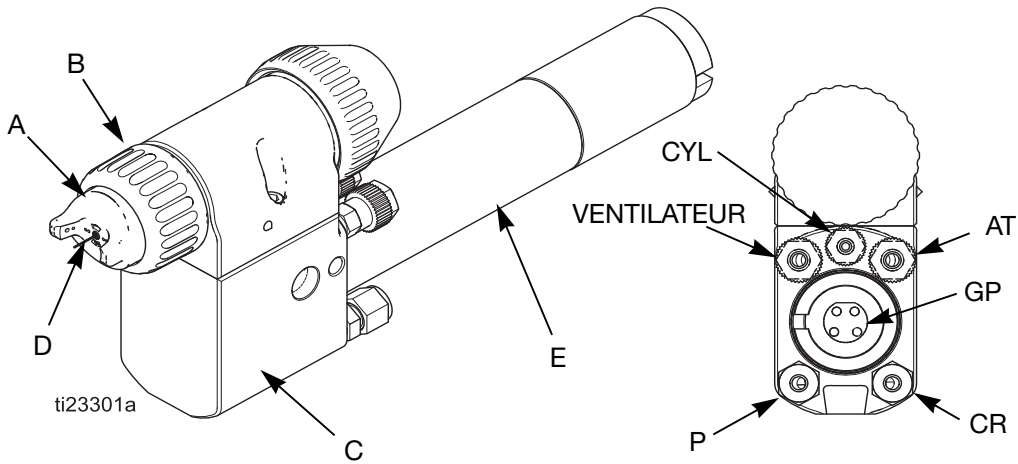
Vue d'ensemble du pistolet (montage par l'arrière)
